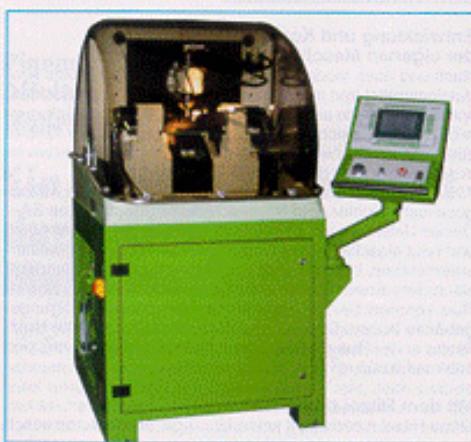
Tailleuse Wahl W100 CNC 8 axes avec commande numérique CNC et trois moteursbroches 15.000 min⁻¹. Wälzfräsmaschine Wahl W100 CNC, 8 CNC-gesteuerte Achsen und drei Motorspindeln 15.000 U/min. Wahl W100 gear hobber with 8-axis CNC numerical control and three 15.000 rpm motorised spindles.
